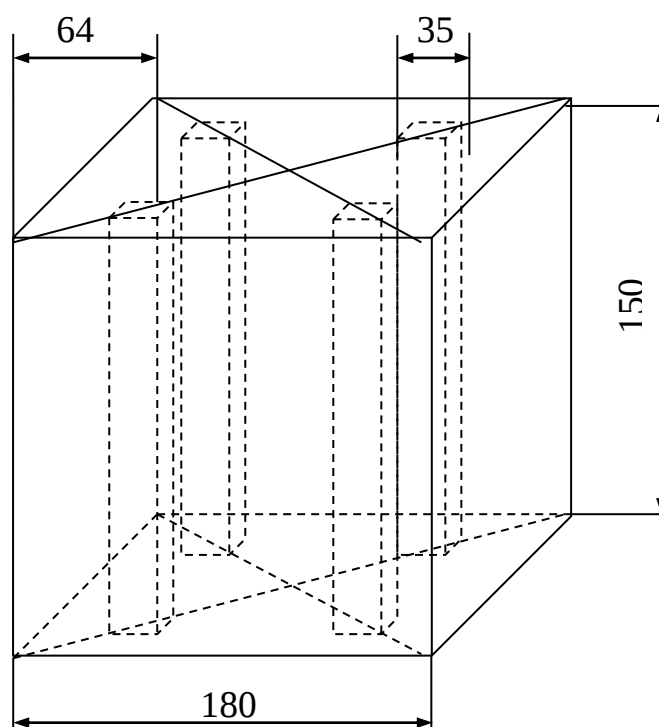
Схема вырезки образцов для исследования гомогенизации и изготовления заготовок для лабораторной прокатки стали ШХ15СГ.
